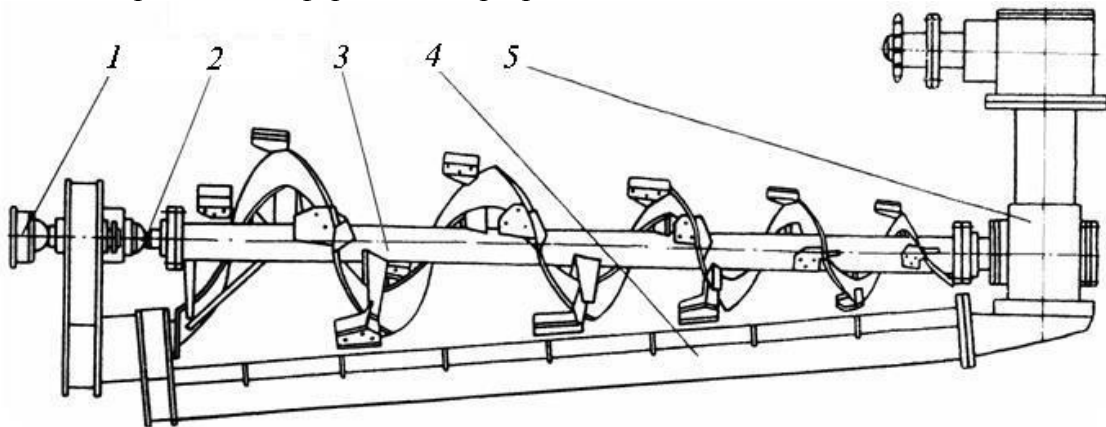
Конічний шнек в зборі з рамою і редуктором:
